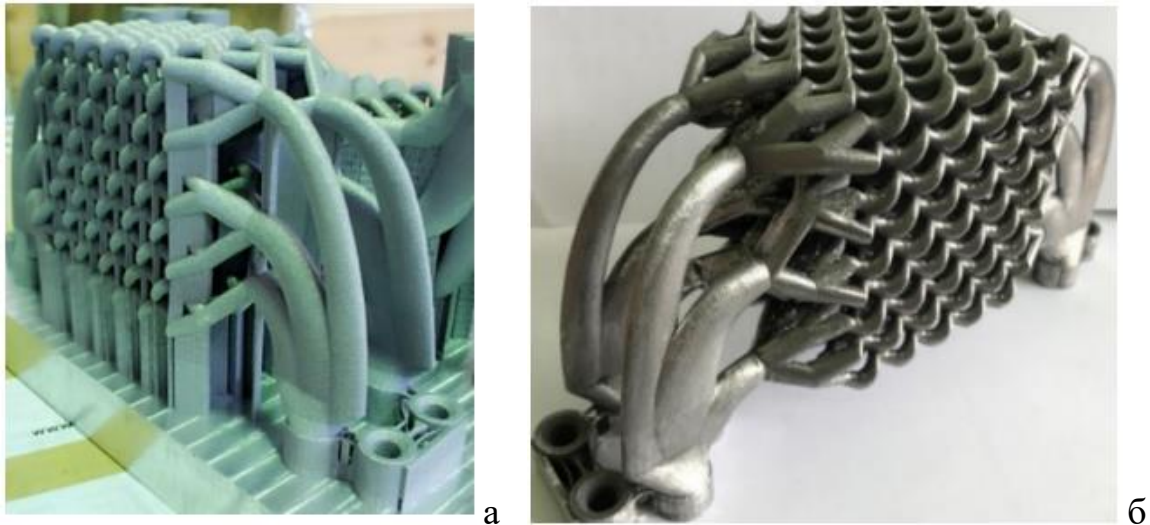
Образец ВДТА: а) 3Д модель фото после изготовления АТ с поддержками; б) после ручной фрезерной обработки и шлифовки
